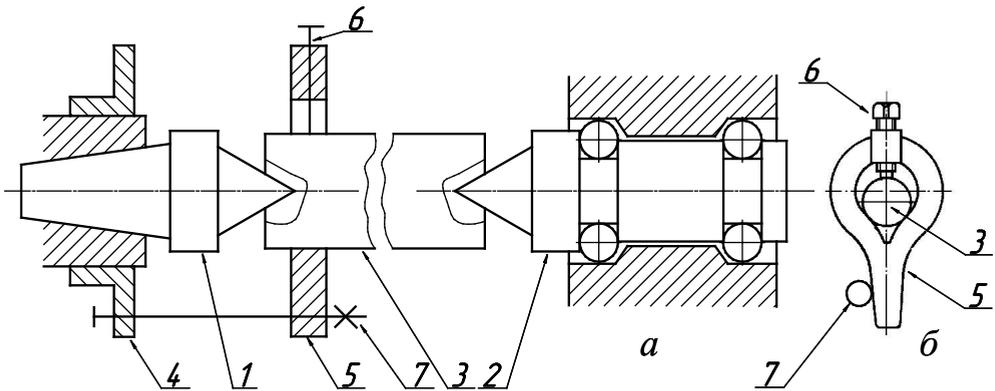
Схема установки вала в центрах с поводковым патроном на токарном станке
